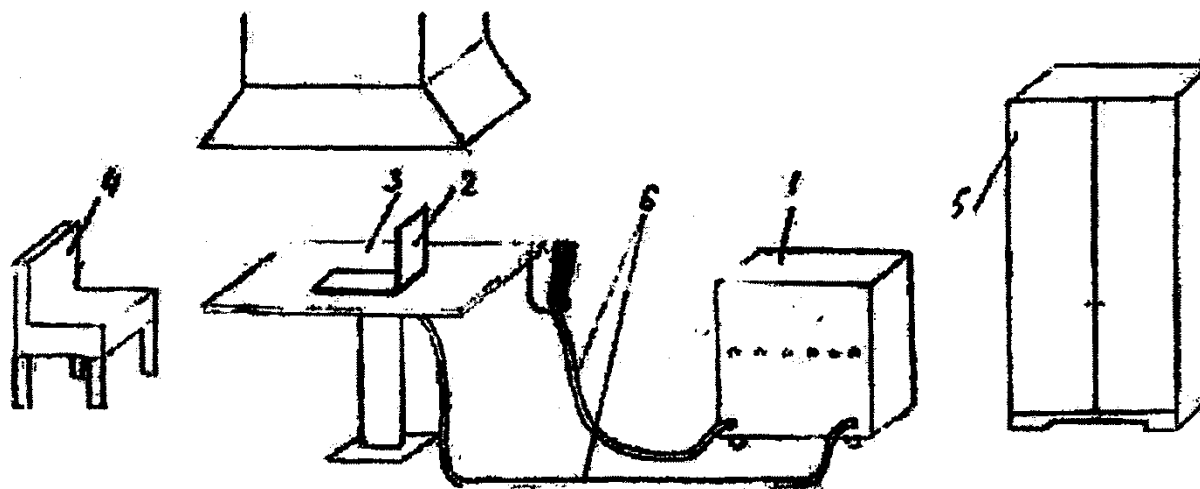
Схема поста для ручной дуговой сварки 1 - источник питания, 2 - изделие, 3 - стол, 4 - стул, 6 - провода
